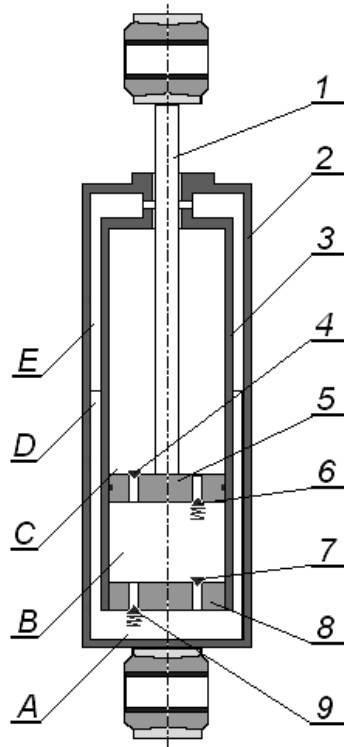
Будова двотрубного газонаповненого амортизатора: 1 – шток; 2 – корпус; 3 – робочий циліндр; 4 – зворотний клапан на поршні; 5 – поршень; 6 – дросельний клапан на поршні; 7 – зворотний клапан донний; 8 – донний клапанний вузол; 9 – дросельний клапан донний; А – кільцеподібна компенсаційна камера; В – нижня робоча камера; С – верхня робоча камера; D – робоча рідина; E – газ
